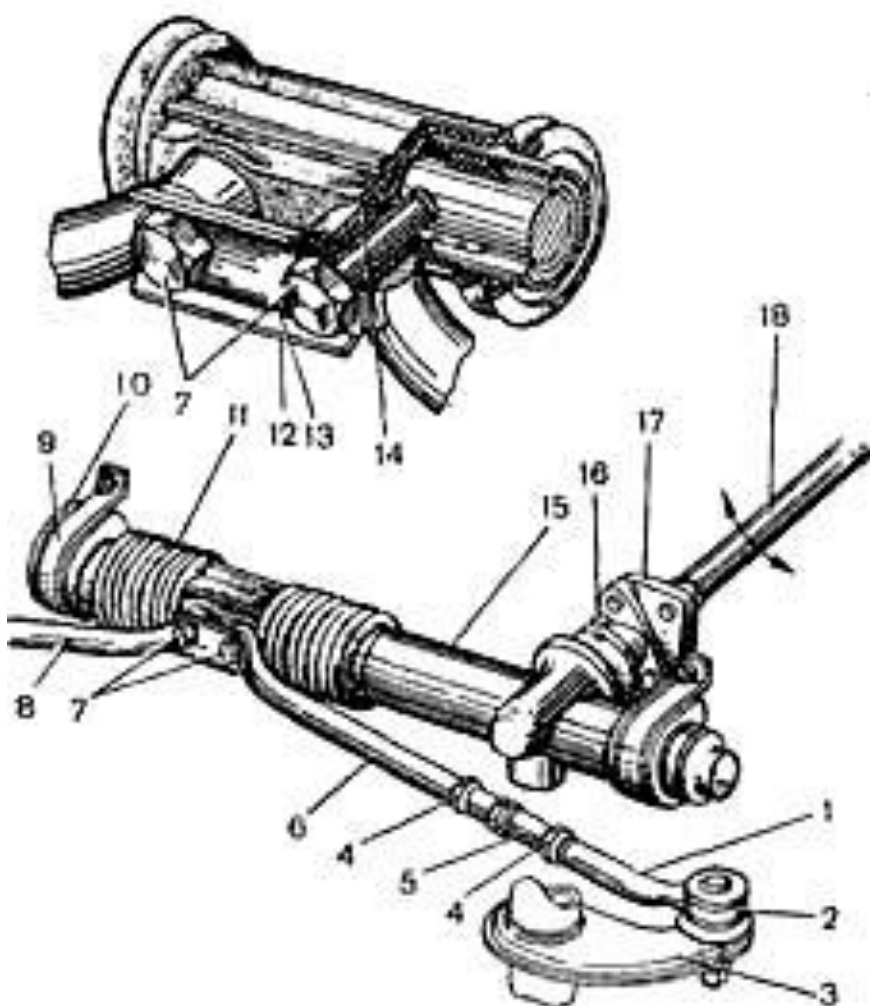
Рулевое управление автомобиля ВАЗ-2109: 1 — наконечник рулевой тяги; 2 — шаровой шарнир наконечника; 3 — поворотный рычаг; 4 — гайка; 5 — регулировочная тяга; 6 — рулевая тяга; 7 — болты крепления рулевых тяг; 8 — правая рулевая тяга; 9 — скоба крепления рулевого механизма; 10 — опора рулевого механизма; 11 — защитный чехол; 12 — соединительная пластина; 13 — стопорная пластина; 14 — резинометаллический шарнир; 15 — картер рулевого механизма; 16 — стяжной болт муфты; 17 — эластичная муфта; 18 — вал рулевого управления
